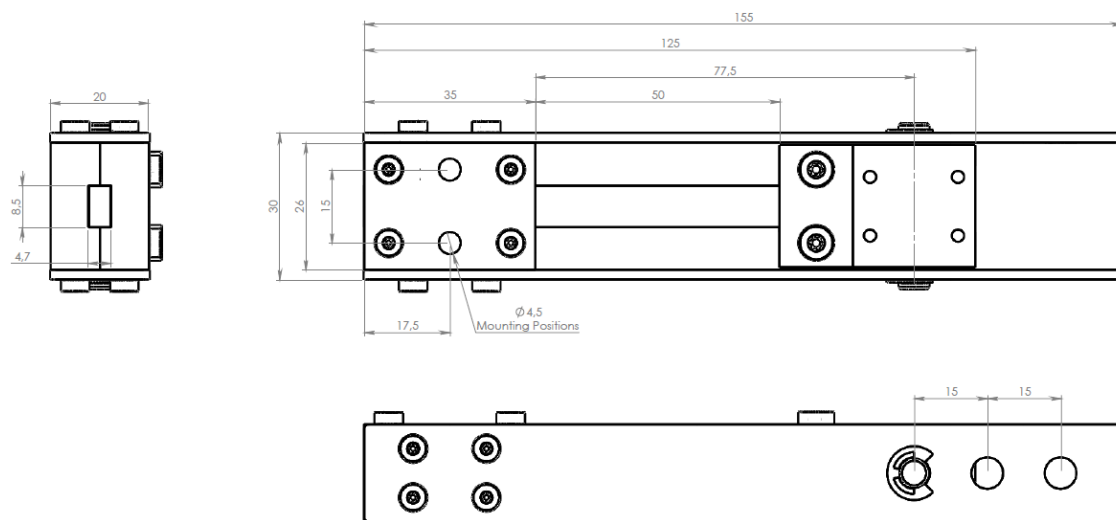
Desenhos do Protótipo ShapeSensor (dimensões em mm)
